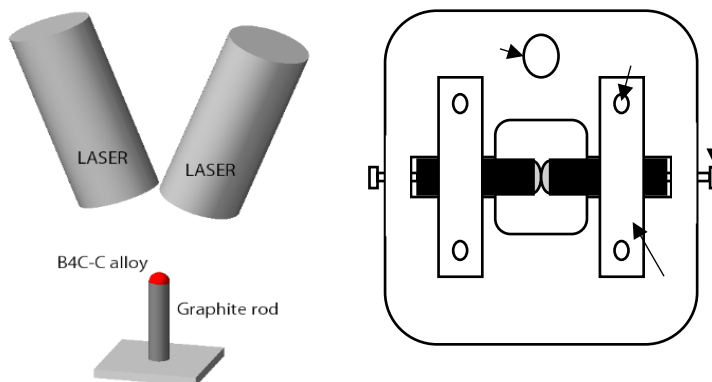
溶接接合試験装置 左：レーザー溶接，右：アーク溶接
